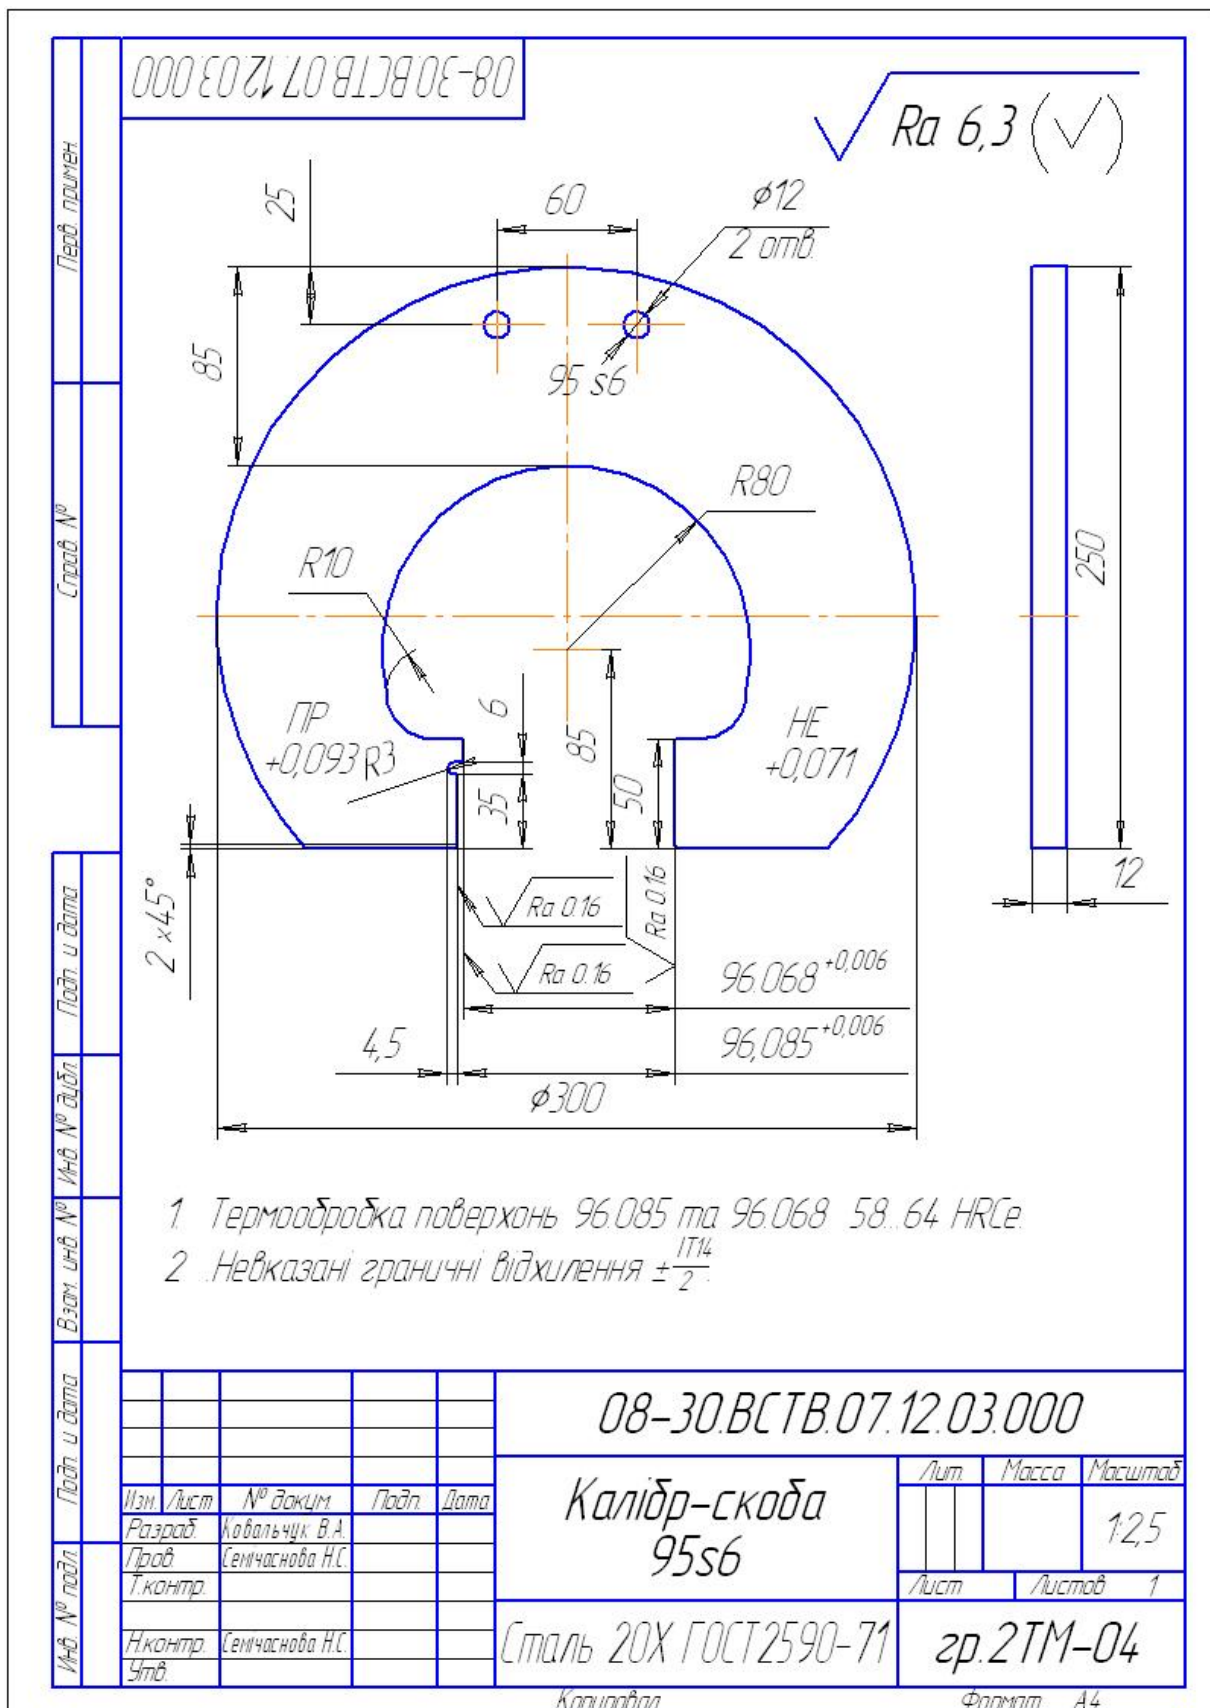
Приклад робочого креслення калібру-скоби для контролю валів
